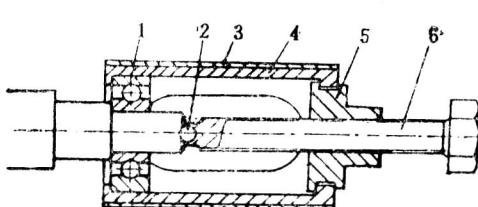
用 I 系列轴承拆卸器拆卸轴承
